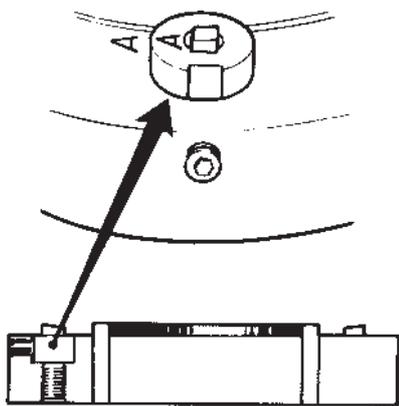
Emplacement du porte-outil dans la tête de fraisage
